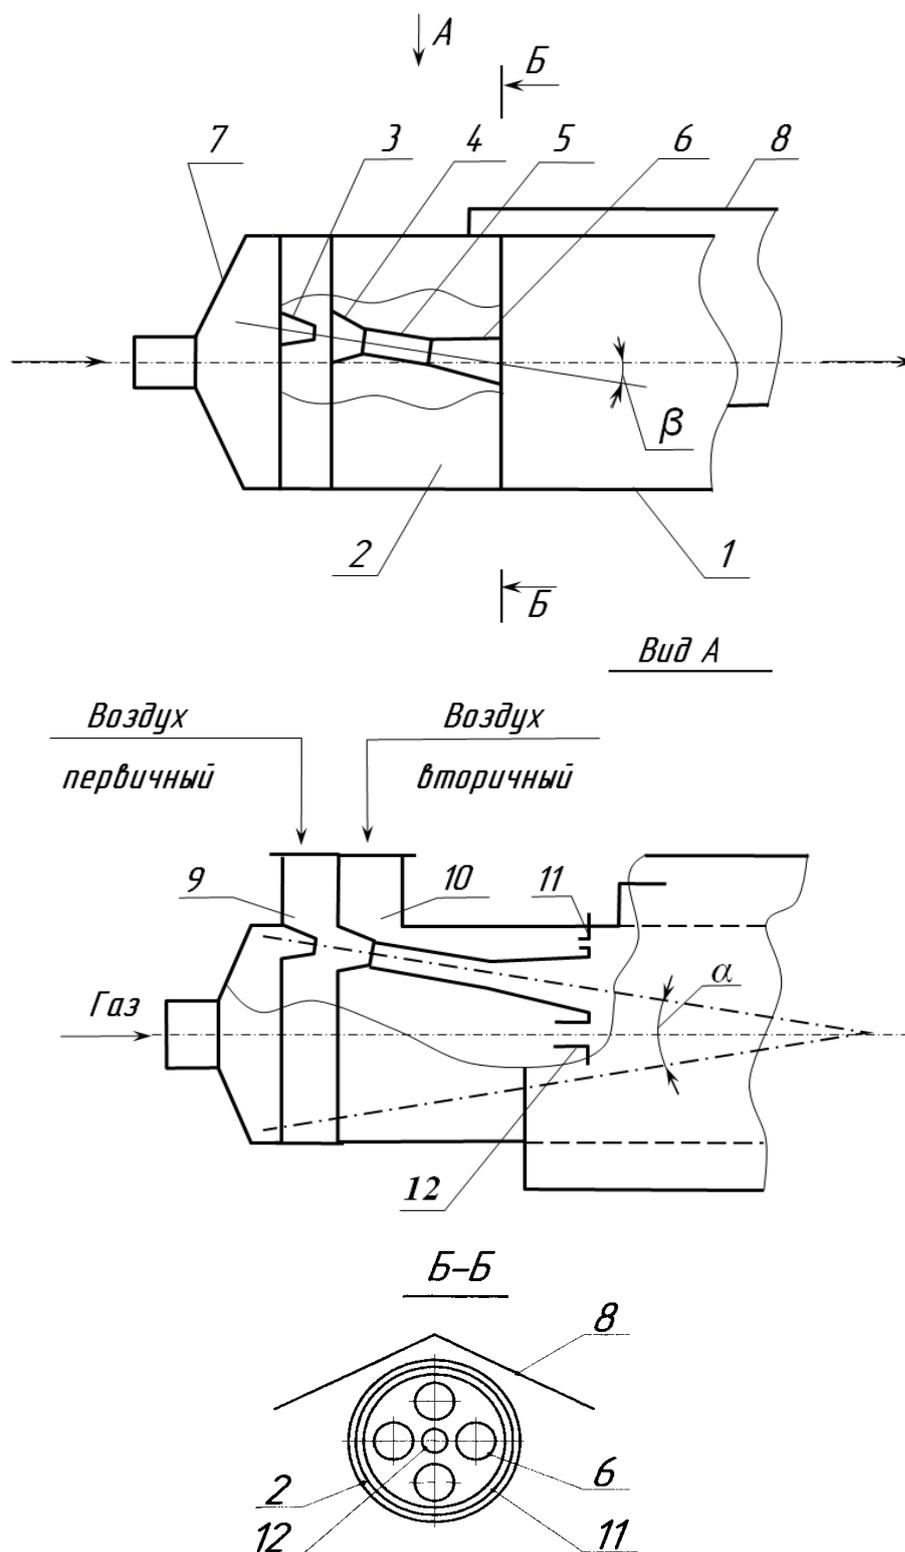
Схема трубчатого инфракрасного нагревателя с полиструйной газовой горелкой:
